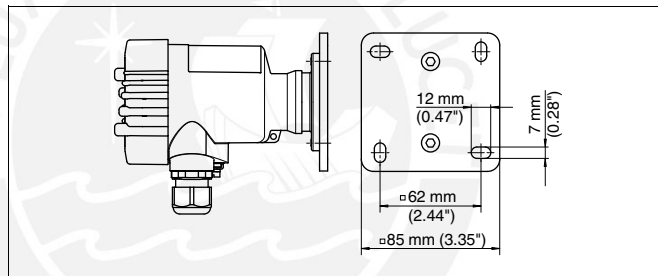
VEGADIS 62 para el montaje en la pared. Vista inferior de la placa de montaje.
